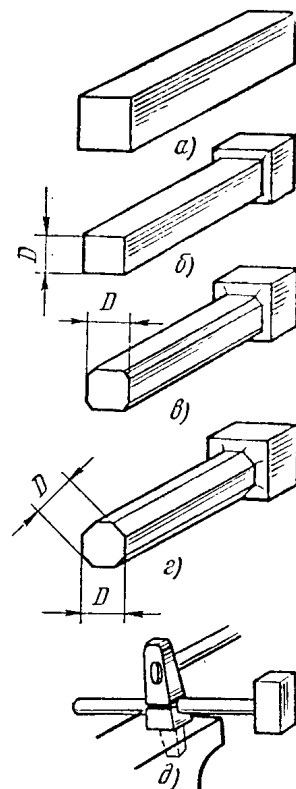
Схема вытяжки квадрата на круглое сечение: а — нагретая заготовка, б — вытянутая на квадрат со стороной D , равной диаметру круга, заготовка, в, г — получение восьмигранника на протянутой части, д — подкатка заготовки круглой обжимкой
